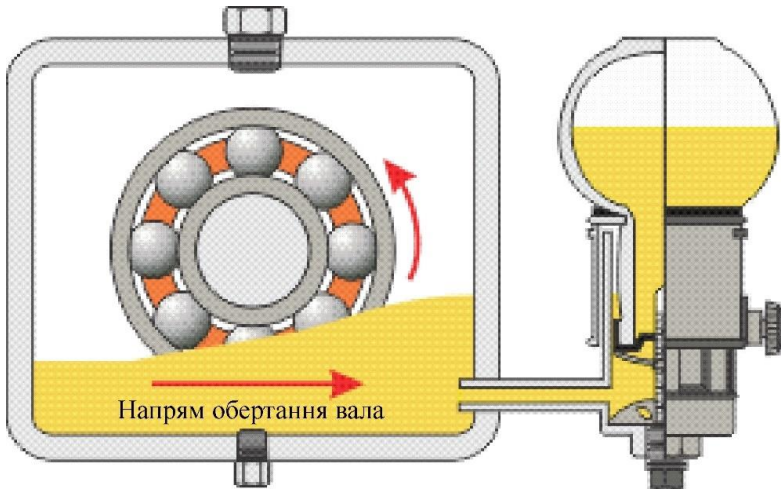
Змащення кулькового підшипника за допомогою Trico Oiler
